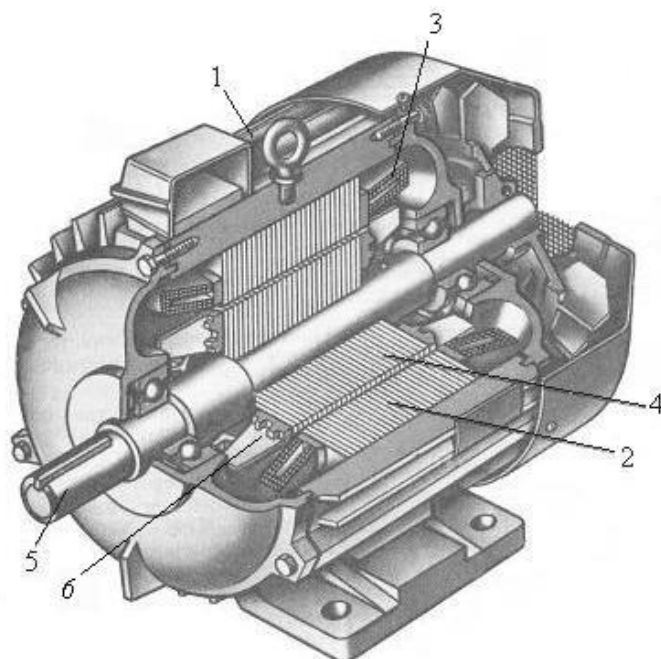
Устройство трехфазного АД с кз-ротором: 1 – корпус; 2 – сердечник статора; 3 – обмотка статора; 4 – ротор с кз-обмоткой; 5 – вал; 6 – кз-кольца с лопатками вентилятора
